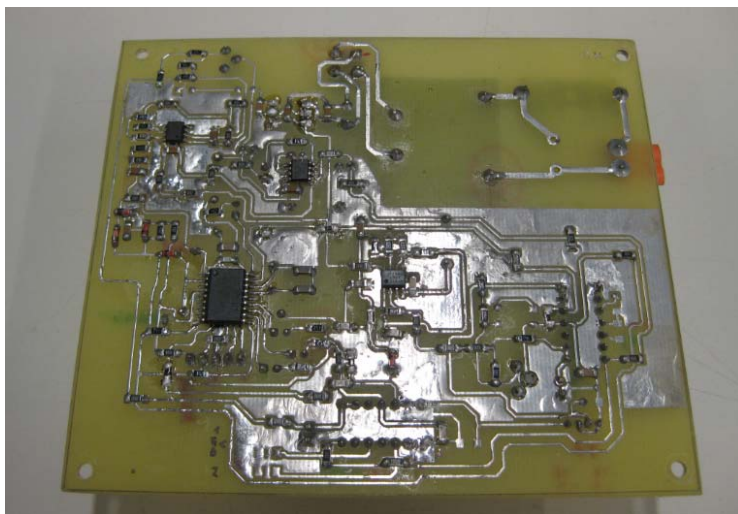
Cara BOT de la PCB amb muntatge component SMD
